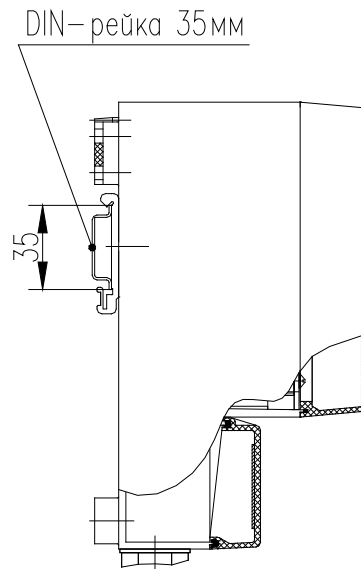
Монтаж БОИ на DIN-рейку.
